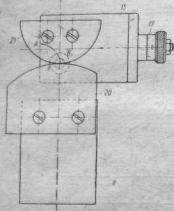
Установка для шлифовки циклоидальной поверхности.
